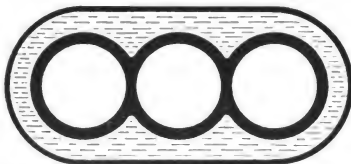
Zylinderblock mit 3 mangelhaft umspülten Zylindern (Wasser kann nicht zwischen den Zylindern durchtreten).
